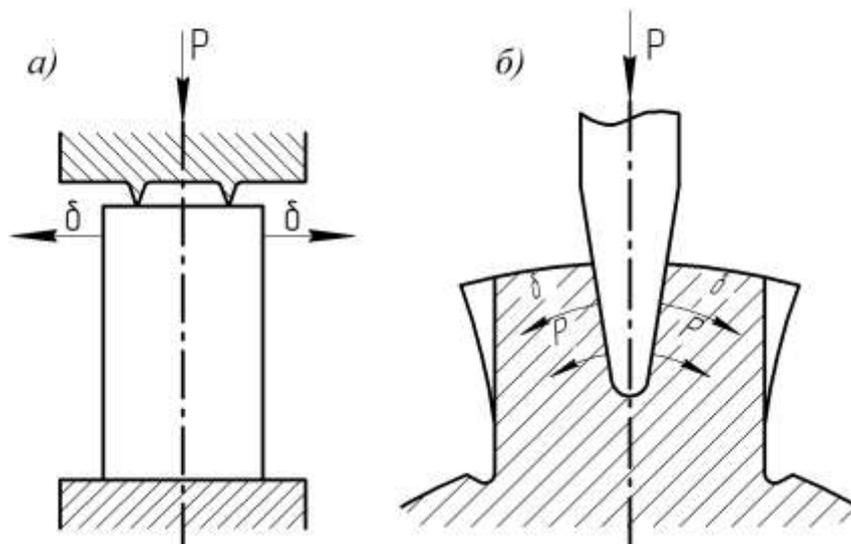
Вдавливание: а – схема обработки; б – приспособление для восстановления шлицев
